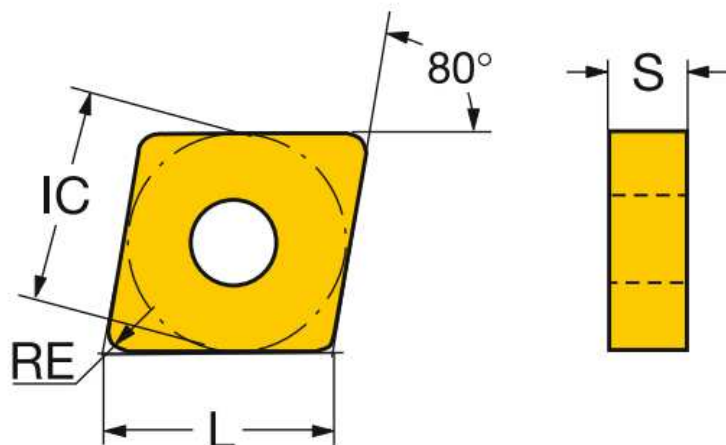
Ромбічна пластина SANDVIK Wiper
